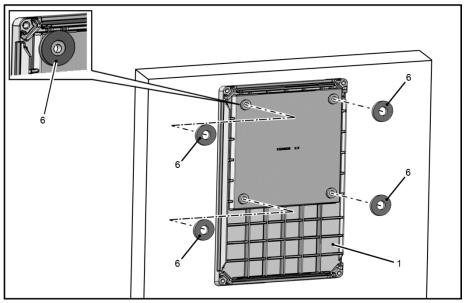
Aufsetzen Flachdichtungen auf Rückseite Adapterplatte
